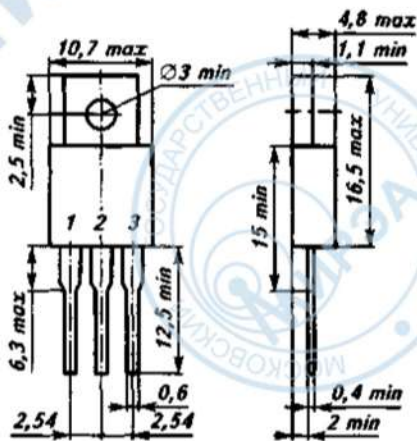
Общий вид, габаритные и присоединительные размеры транзисторов КТ858А и КТ8140А1 в корпусе КТ-28:
